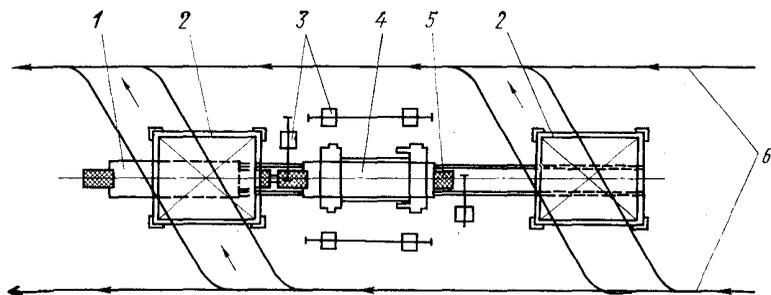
Схема расположения главного кондуктора для сборки кузова автомобиля
